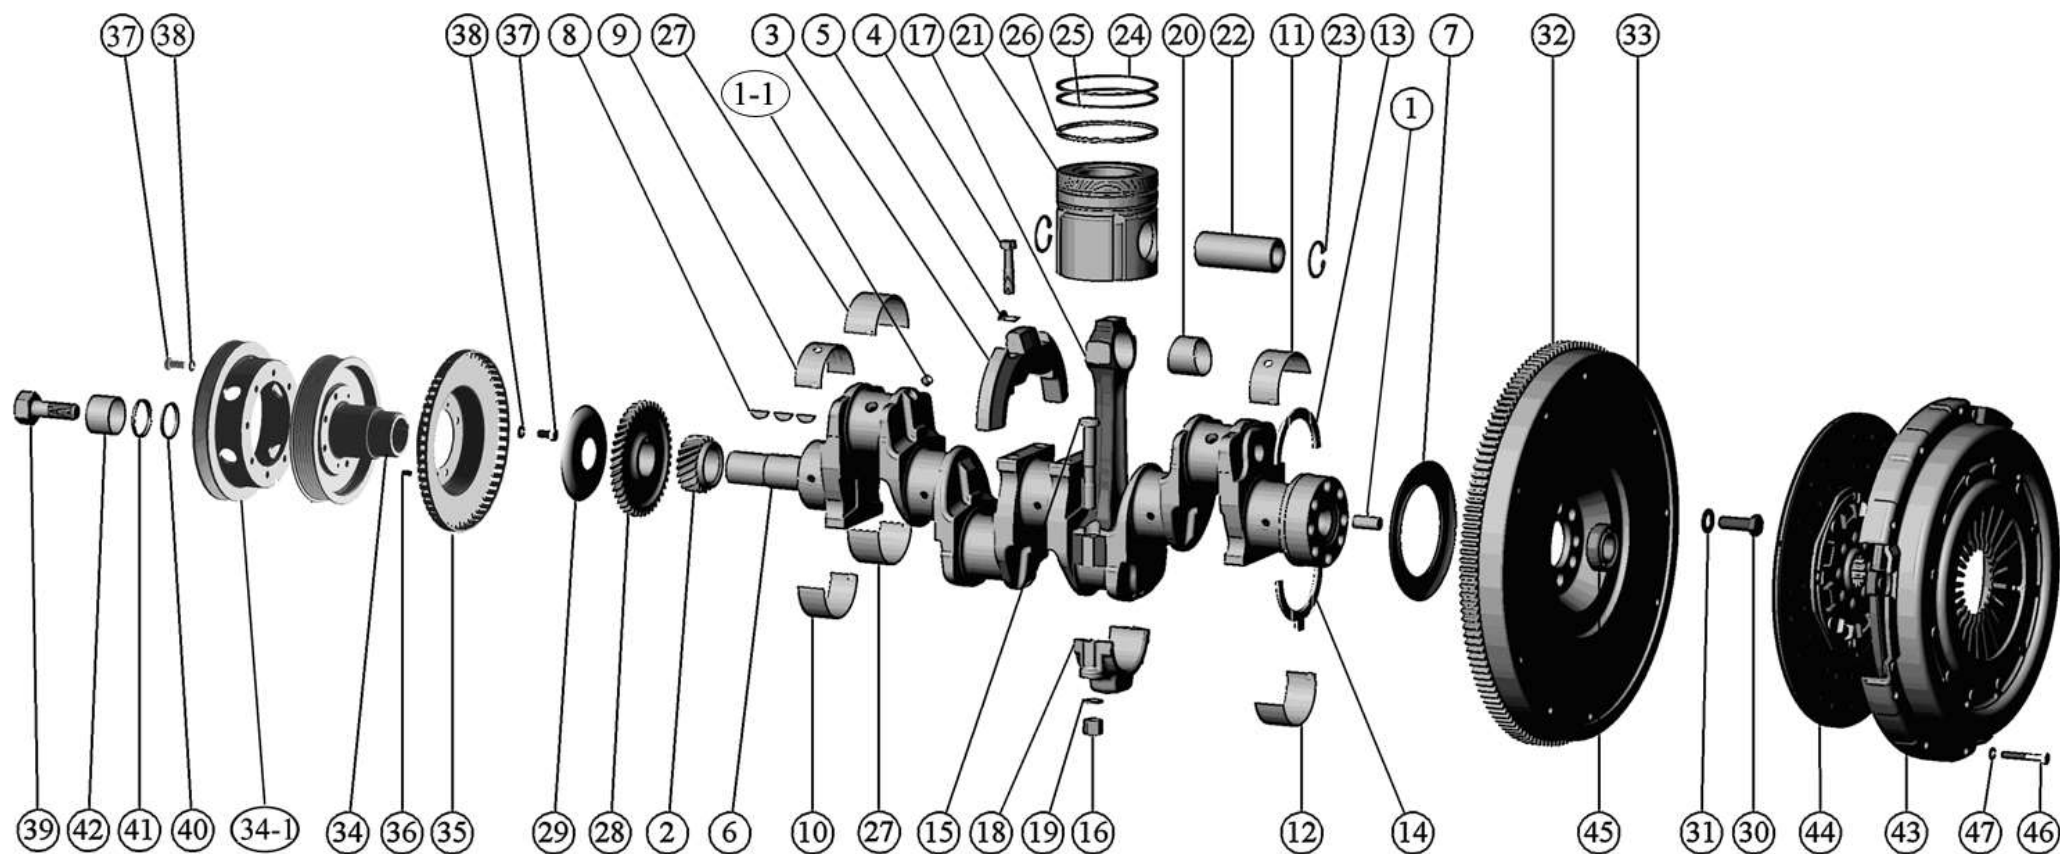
Кривошипно-шатунный механизм. Установка шкива коленчатого вала. Установка муфты сцепления.
